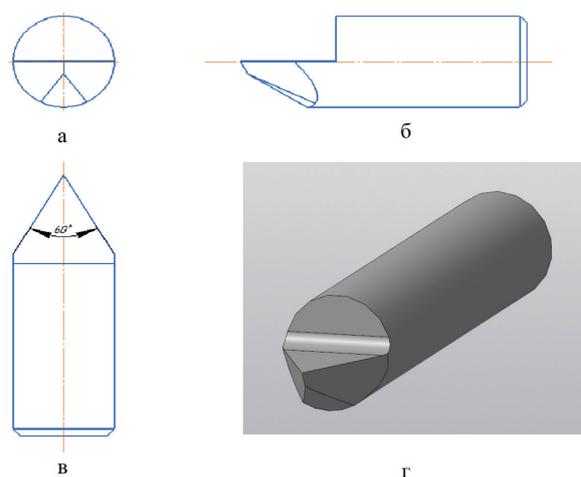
Геометрия специально изготовленного инструмента (а — вид спереди, б — вид сбоку, в — вид сверху, г — 3D модель)
